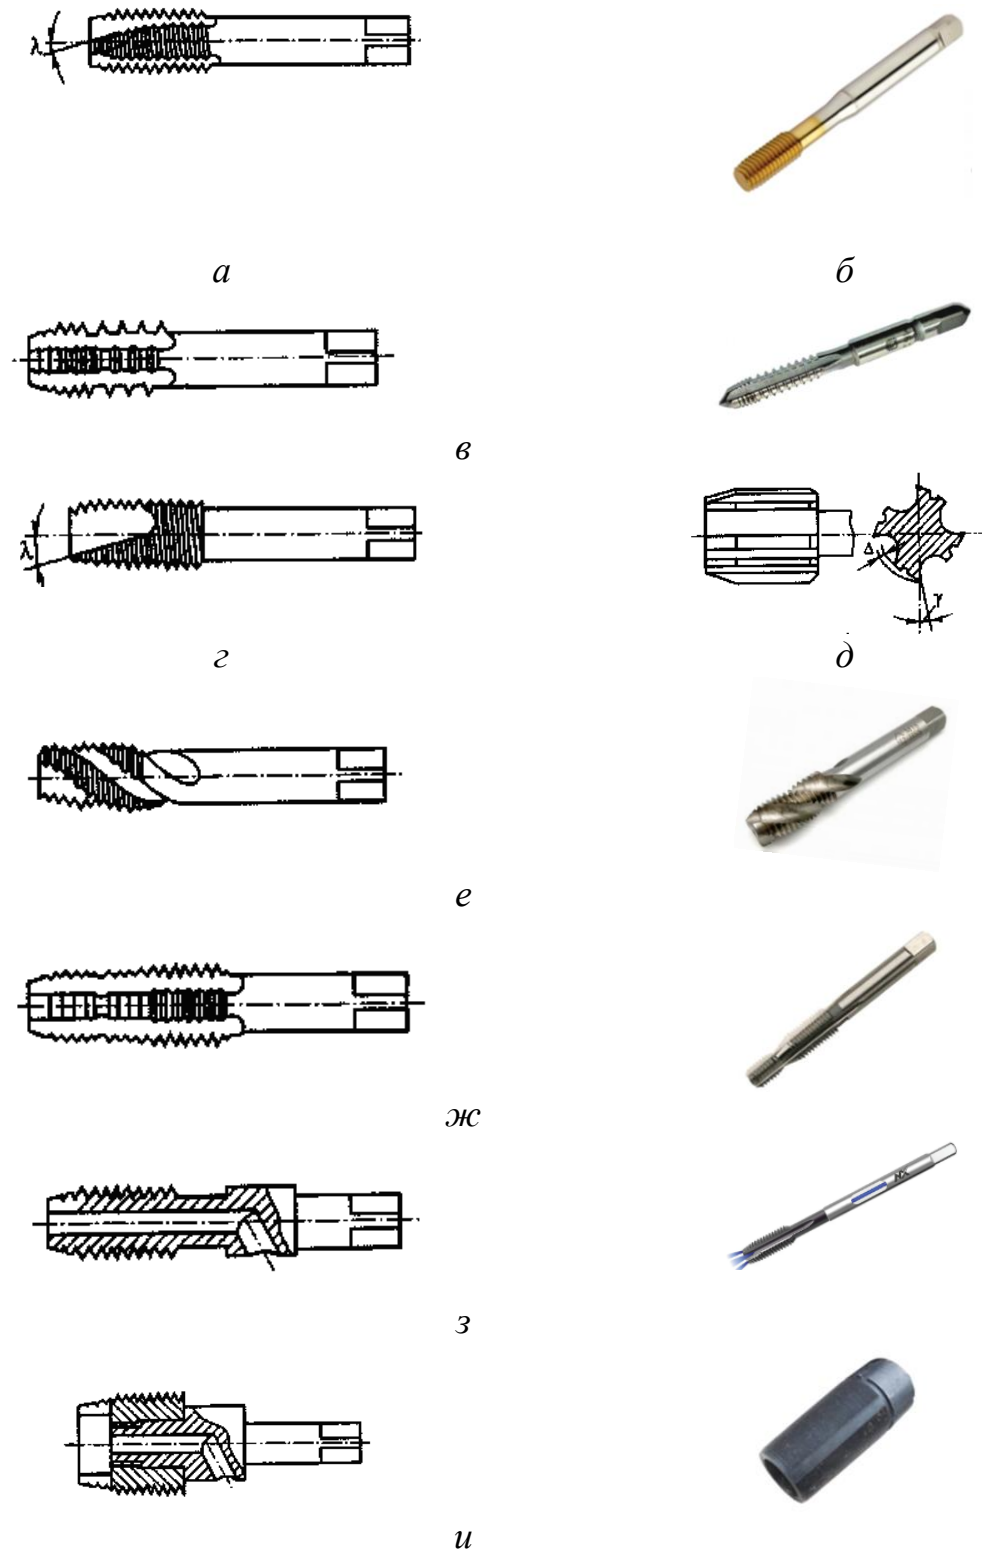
Конструкции некоторых типов метчиков: *а* – машинно-ручной (режущий); *б* – пластически деформирующий (бесстружечный); *в* – с шахматным расположением зубьев; *г* – режуще-деформирующий; *д* – с режуще-выглаживающими зубьями; *е* – с винтовыми канавками; *ж* – ступенчатый; *з* – с внутренним подводом СОТС; *и* – колокольного типа
